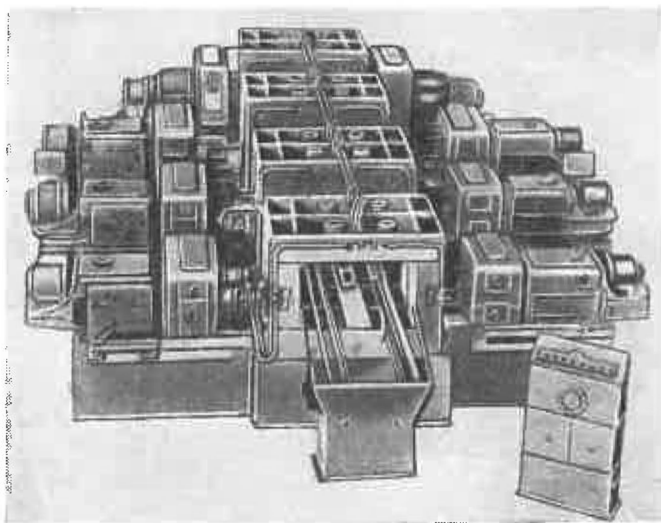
Machine transfert pour l'usinage du bloc cylindres d'un tracteur
